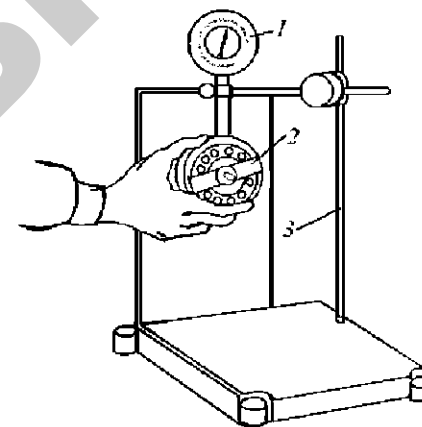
Измерение радиального зазора подшипника: 1 – индикатор; 2 – подшипник; 3 – ступица
